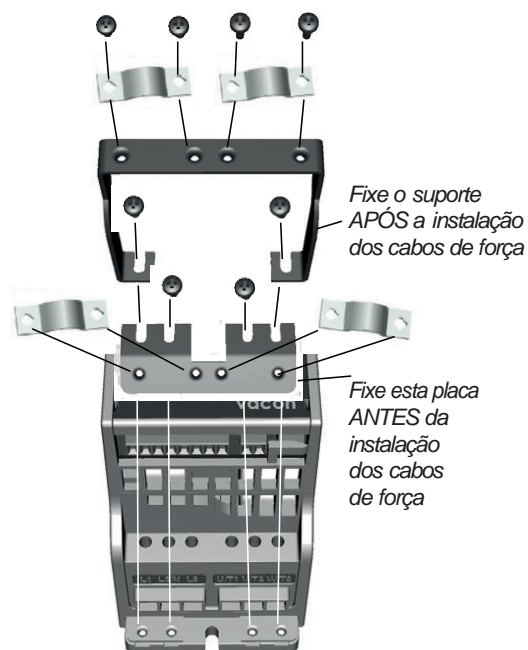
Instalação da placa PE e suporte a cabo API, MI1 - MI3
